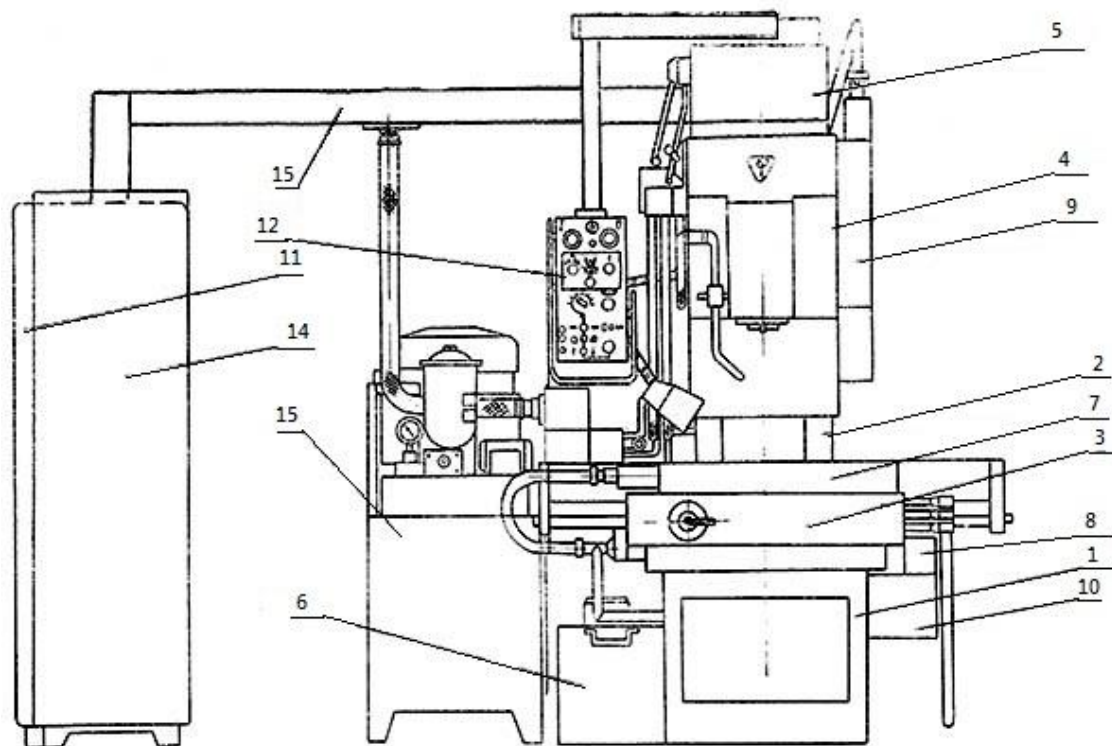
Станок фрезерный бесконсольный 6520ф3:
